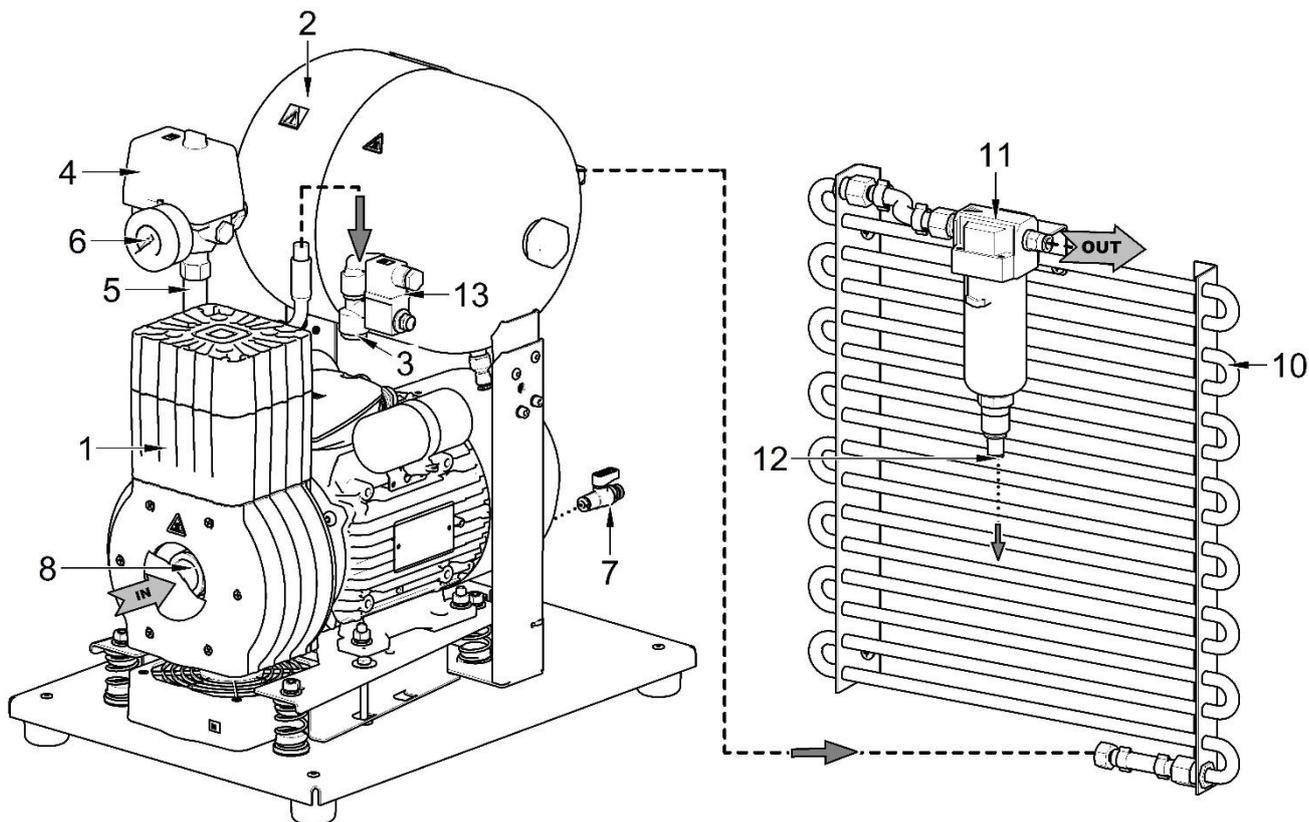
Компрессор DK50-10Z/M с осушителем
